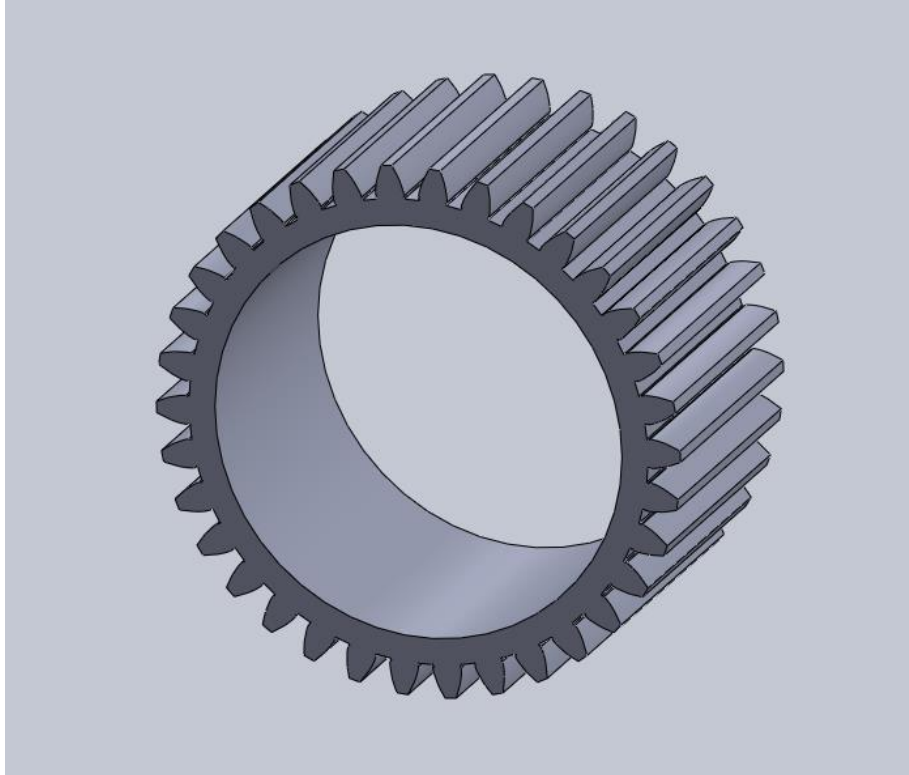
Apariencia final del engrane. Perspectiva dimétrica.
